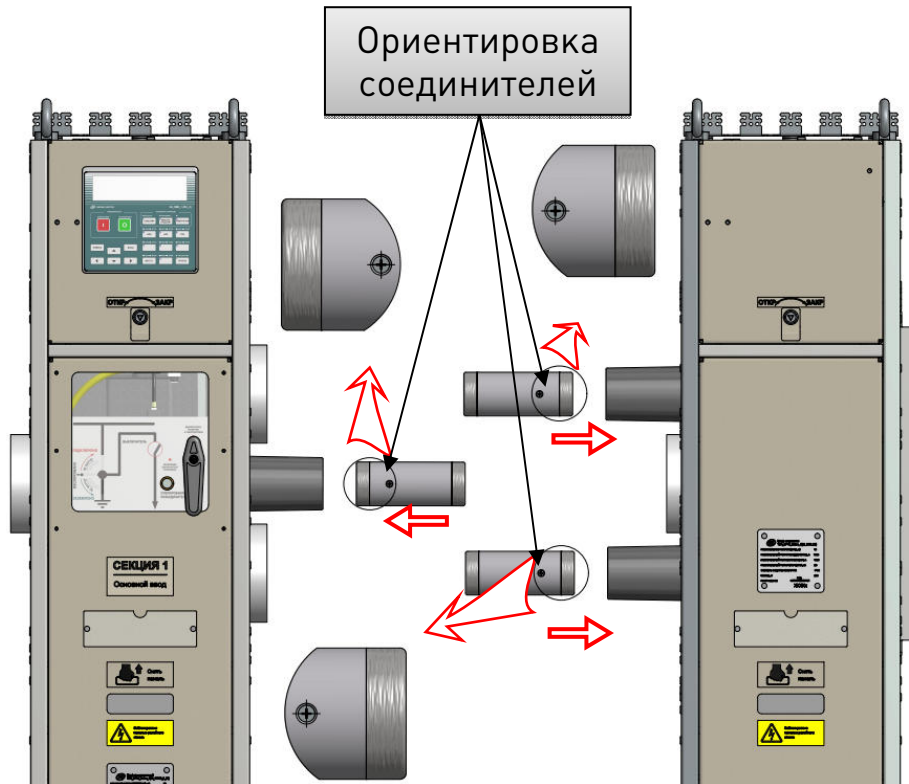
Установка изоляции соединителей СШ с правой стороны шкафа
